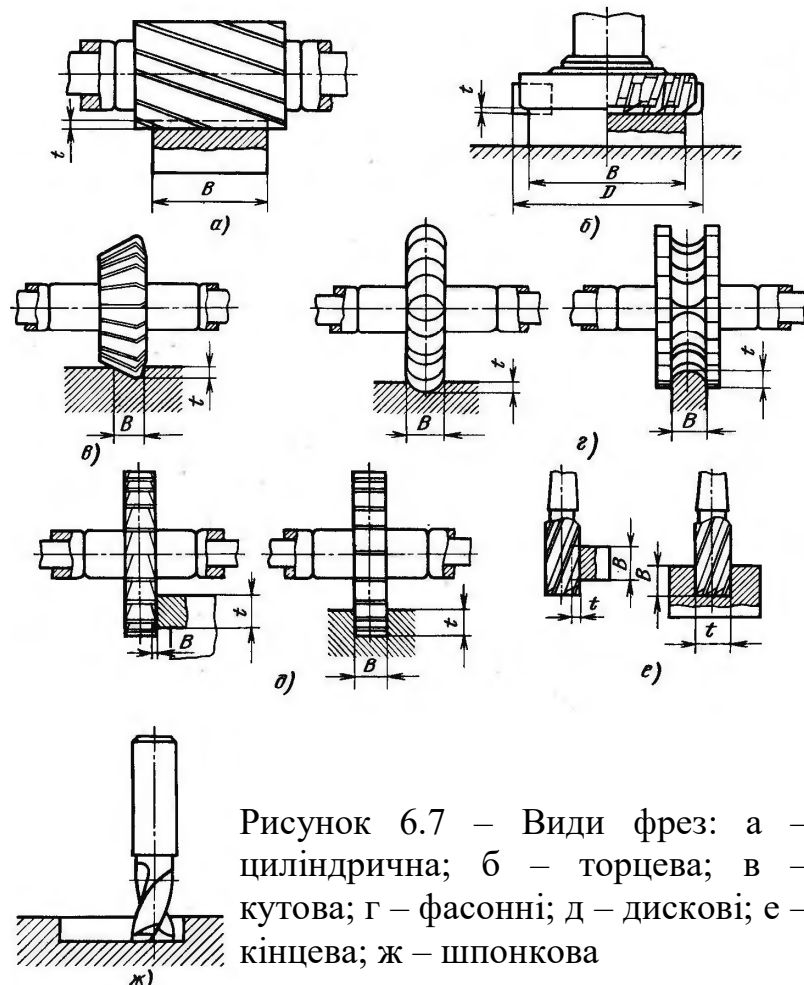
Види фрез: а – для чорнової обробки циліндрична; б – торцева; в – при великих глибинах кутова; г – фасонні; д – дискові; е – кінцева; ж – шпонкова
